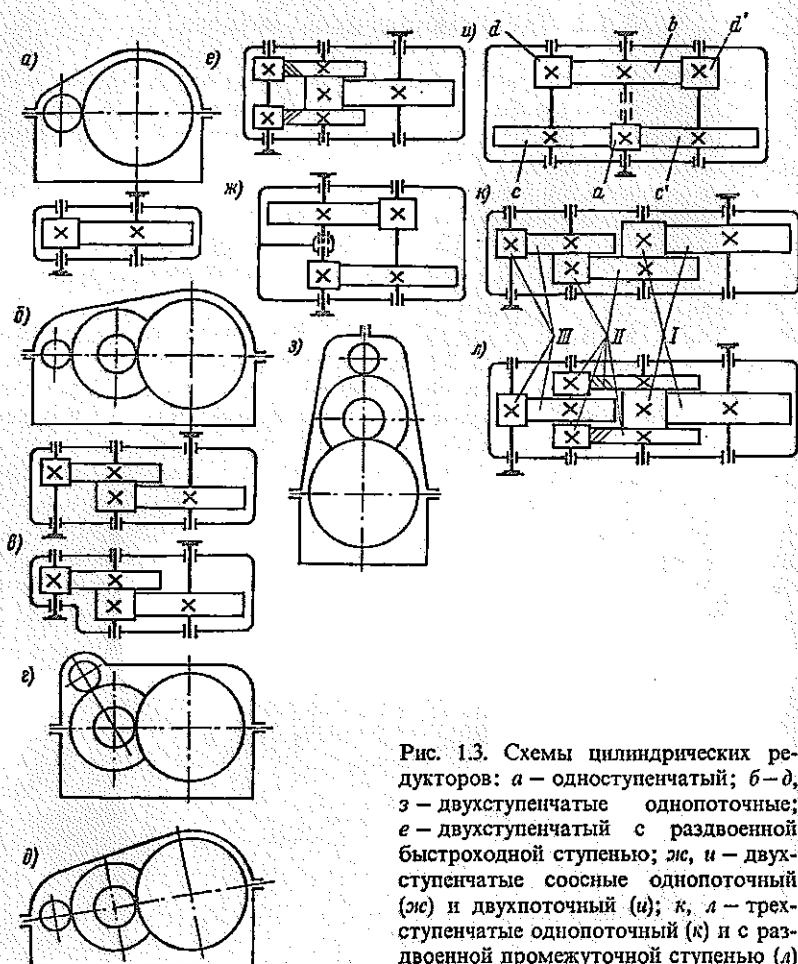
Схемы цилиндрических редукторов: а — одноступенчатый; б—д, з — двухступенчатые однопоточные; е — двухступенчатый с раздвоенной быстроходной ступенью; ж, и — двухступенчатые соосные однопоточный (ж) и двухпоточный (и); к, л — трехступенчатые однопоточный (к) и с раздвоенной промежуточной ступенью (л)
